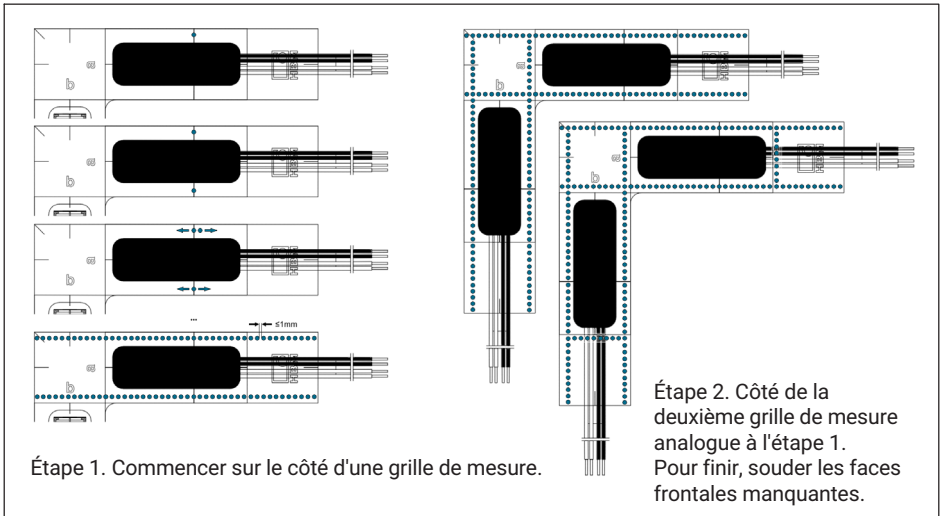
Séquence de soudage de la TS81 HT
